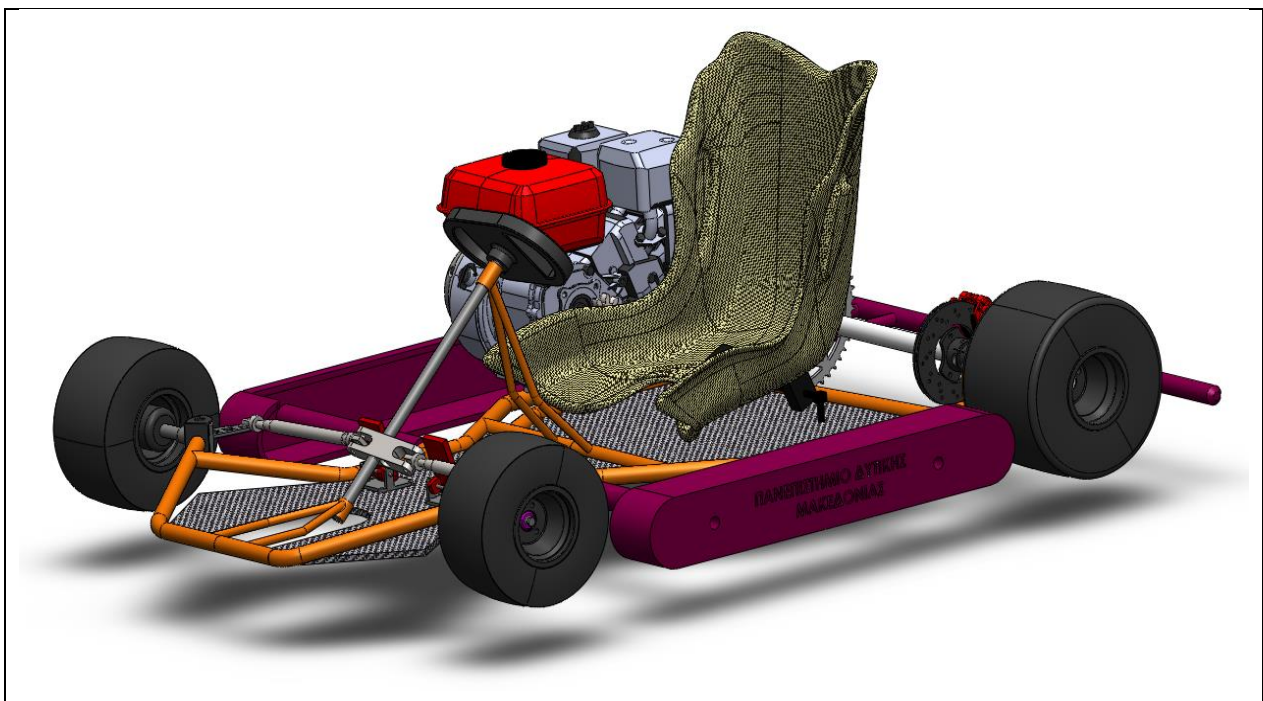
Ολοκληρωμένο σχέδιο Assembly Kart οχήματος (Right Plane)
